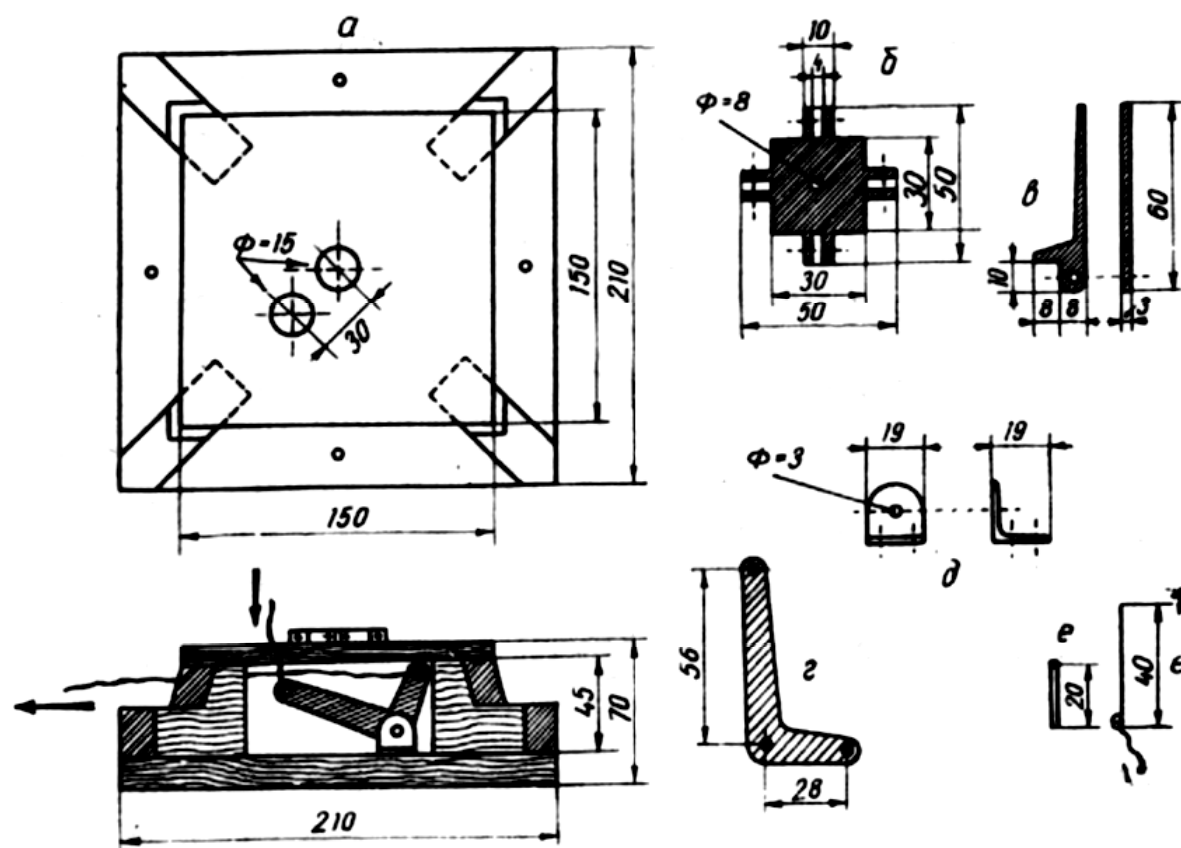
Деталі стартового пристрою: а) стартова платформа (вигляд зверху); б) основа герметичного замка; в) лапки-затискачі (4 шт.); г) кутник для висмикування чеки; д) основа кутника (2 шт.), е) патрубок чеки; е) чека.
